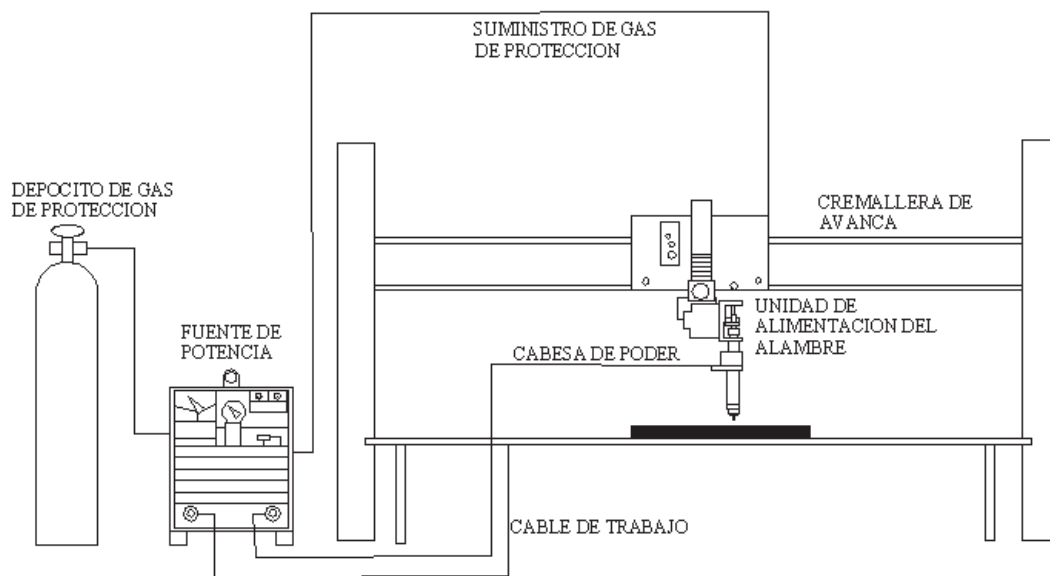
15 Montaje del proceso de soldadura GMAW con sistema de avance de antorcha mecanizado.
